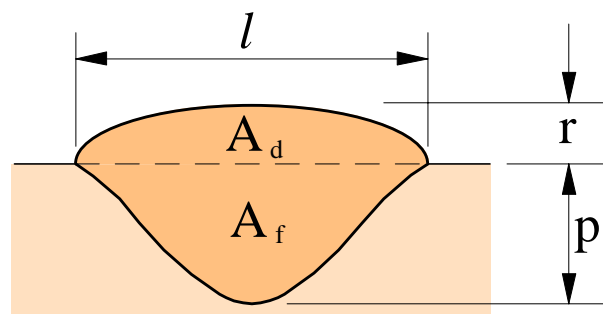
Características geométricas de um cordão de solda: p - penetração, r - reforço, l - largura, A_d - área depositada, A_f - área fundida.
